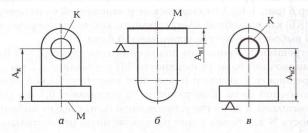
Последовательность обработки поверхностей: a — чертеж конструктора;  $\delta$  — обработка плоскости; b — обработка отверстия
